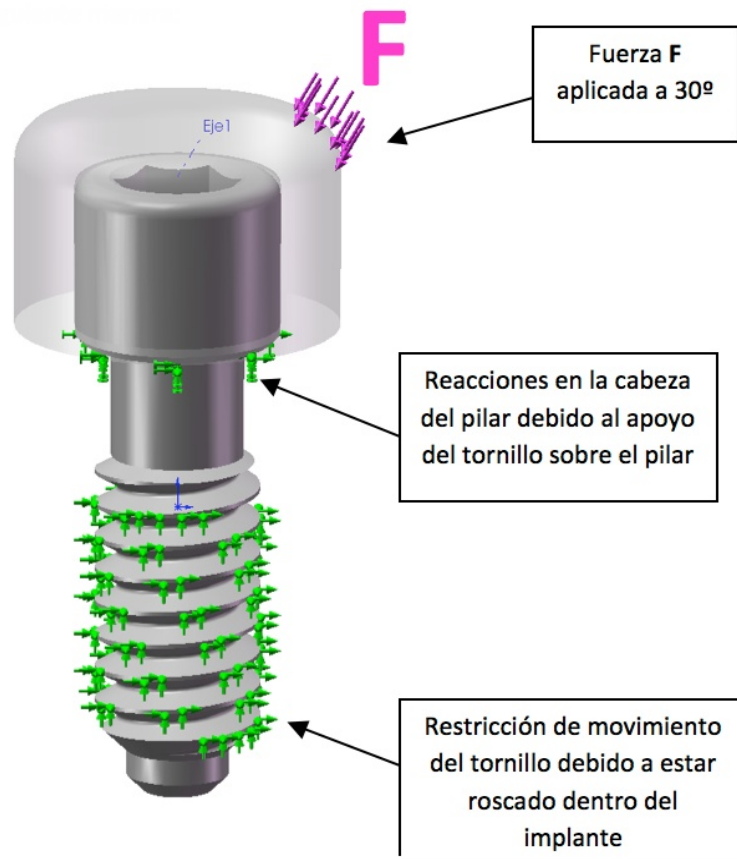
Esquema del diseño del ensayo mediante AEF del tornillo control.
